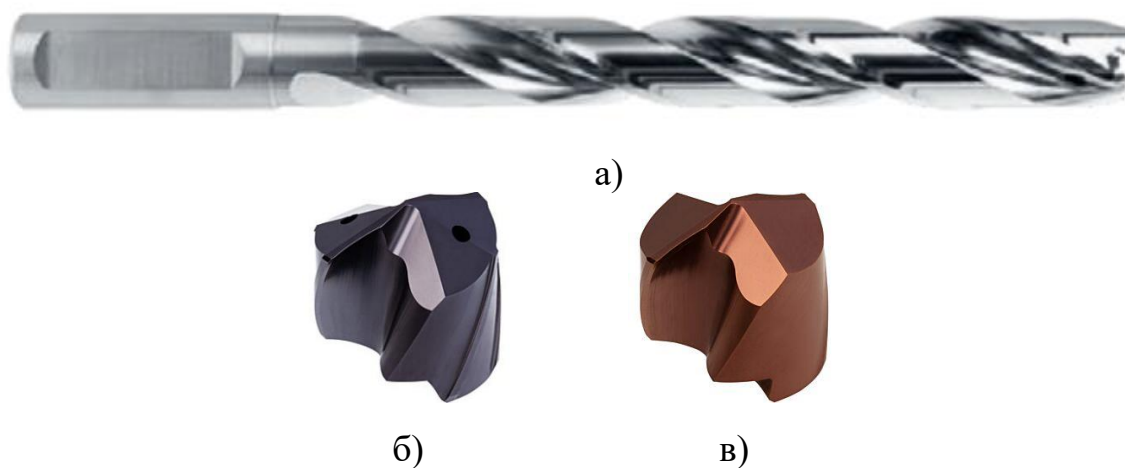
Свердлильна система BT 800 для $\varnothing 10,00 - \varnothing 26,499$ мм:
